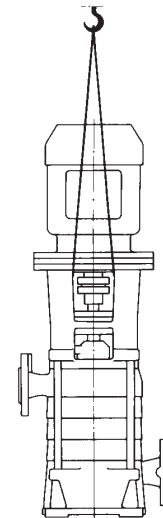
Транспортировка насосного агрегата с вертикальным размещением
